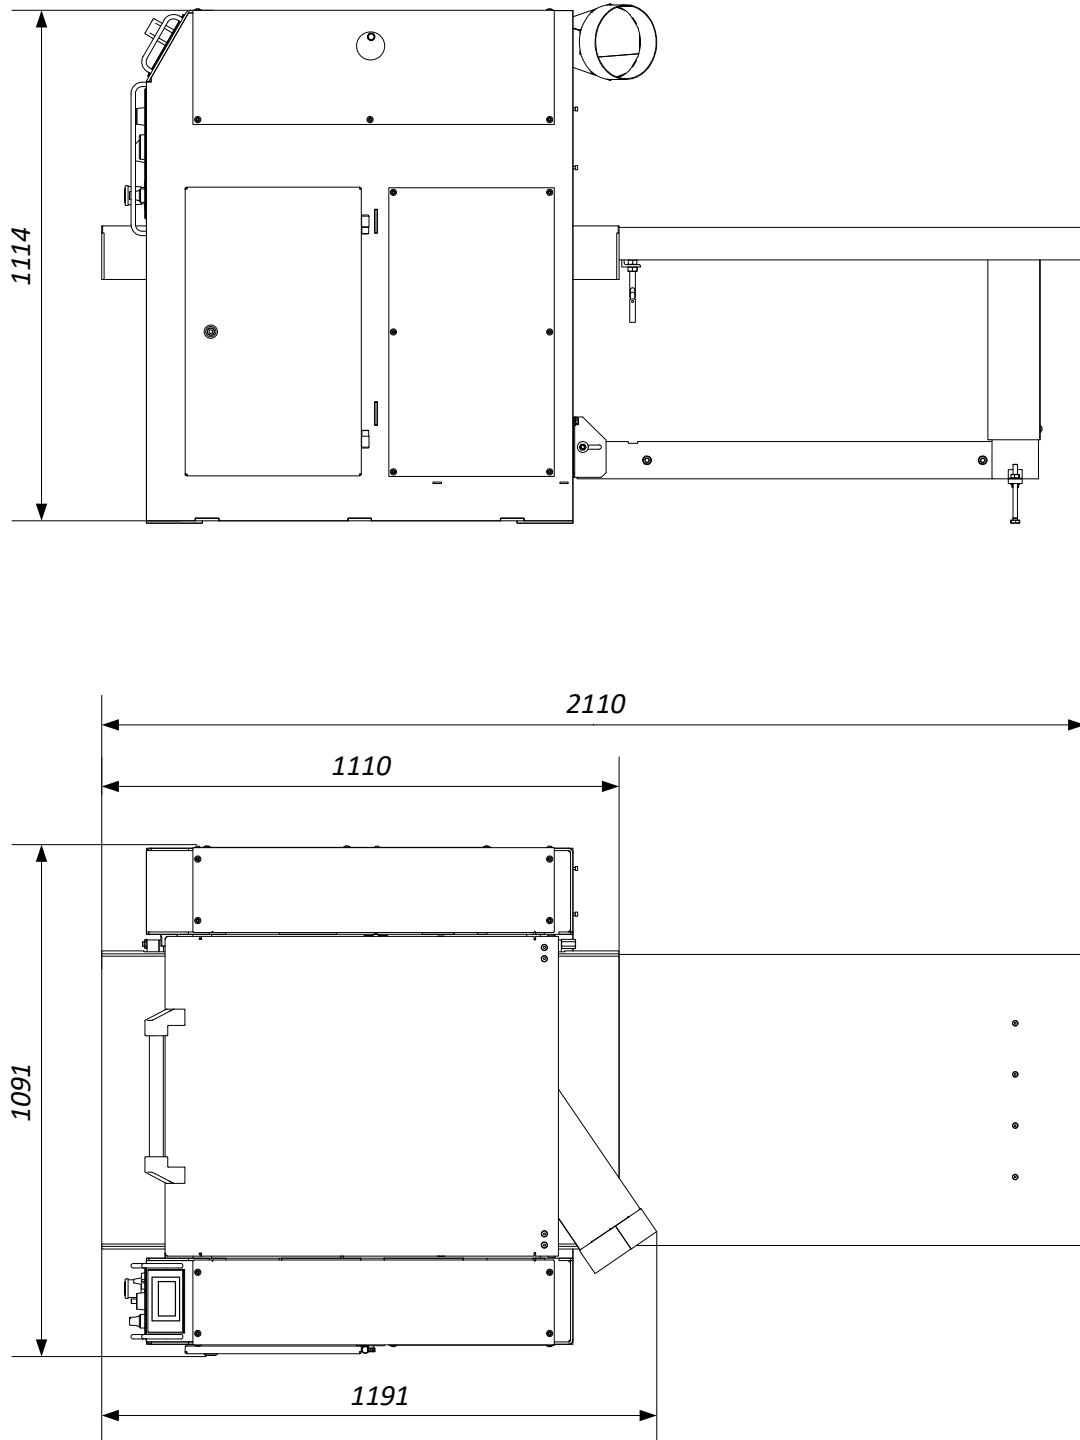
Abmessungen - Seitenansicht / Draufsicht
